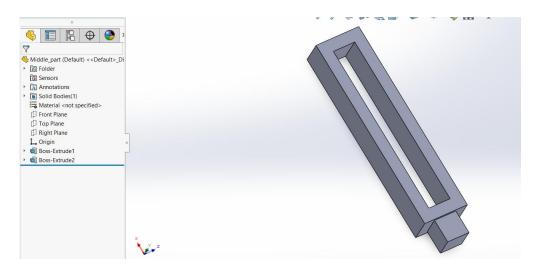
Основна велика рухома деталь принтера
